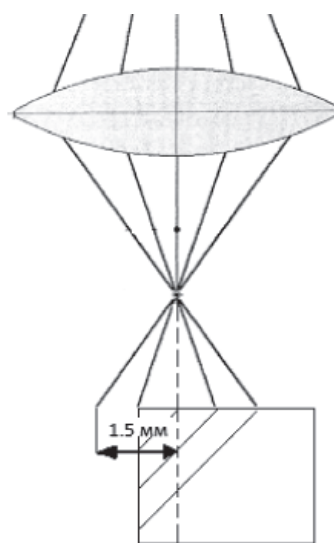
Схема фокусировки и расположения лазерного луча относительно обрабатываемых поверхностей
